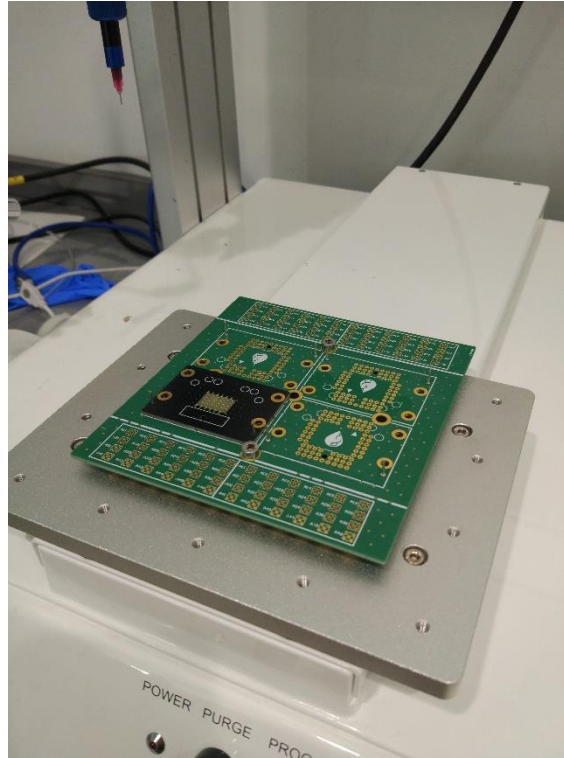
PCB atornillada a la base del robot para la colocación de la PCB de contactos durante el proceso de dispensación
